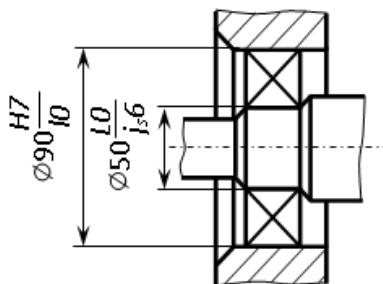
Отображение посадок для обоих колец подшипника качения
